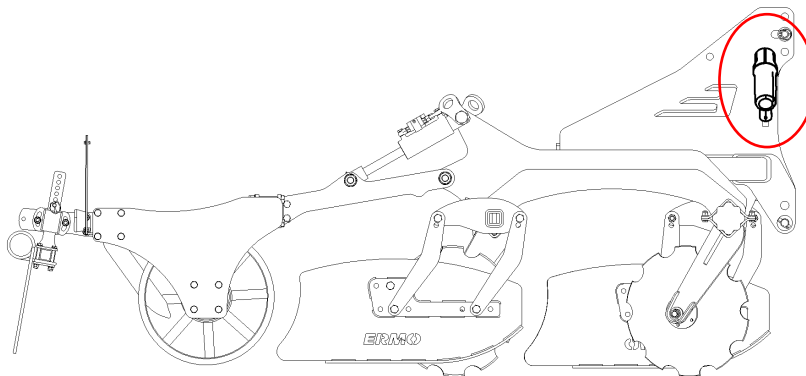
Posizione del tubo portadocumenti sulla testata / Position of the document holder of the machine head.
